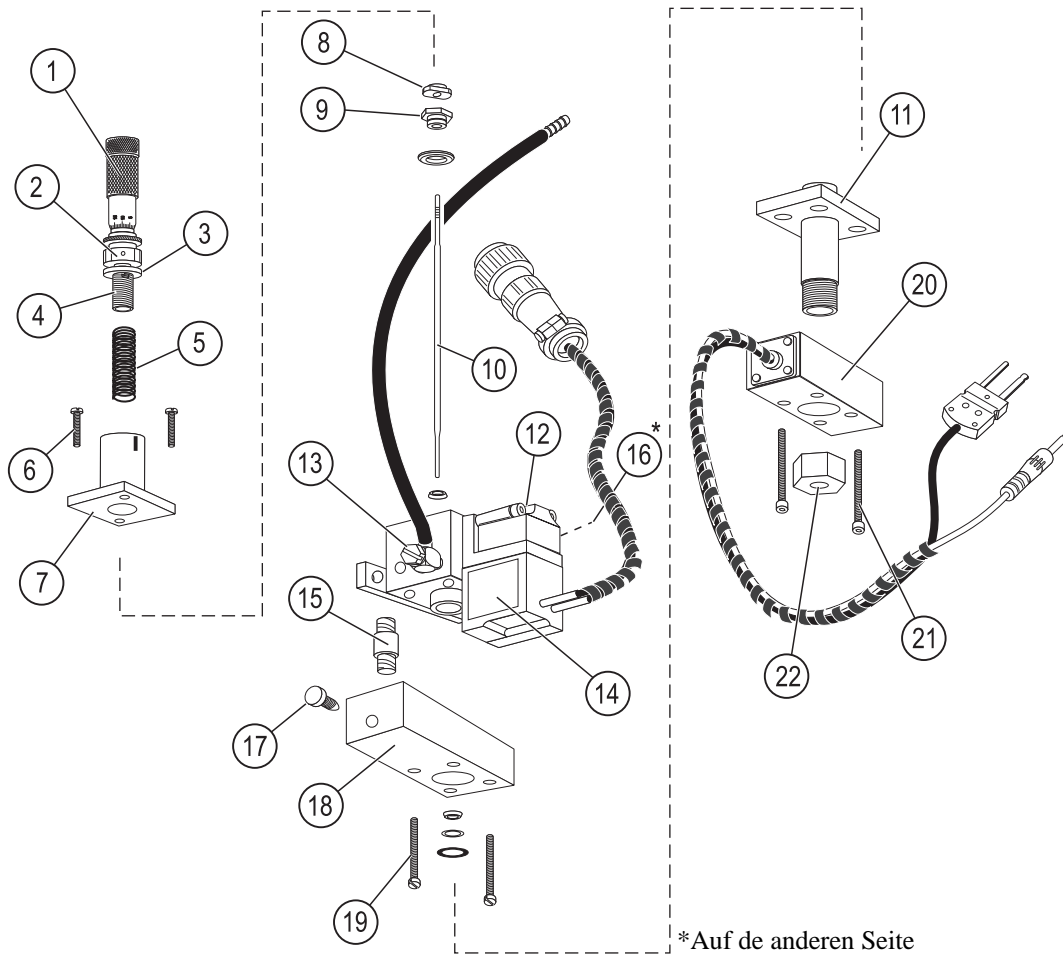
DispenseJet Serie DJ-2100 Explosionszeichnung
